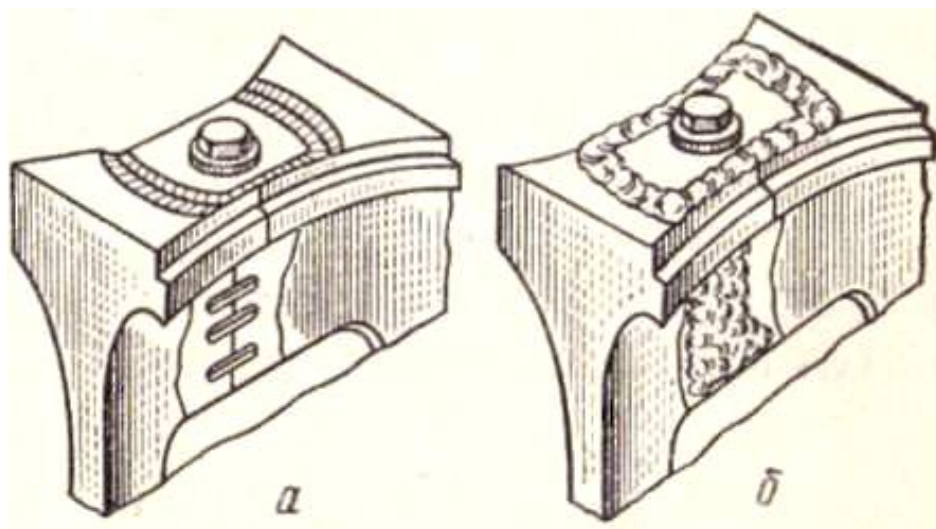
Підготовка тріщини в перемичці між циліндрами до заварки (а) і перемичка після заварки (б).
